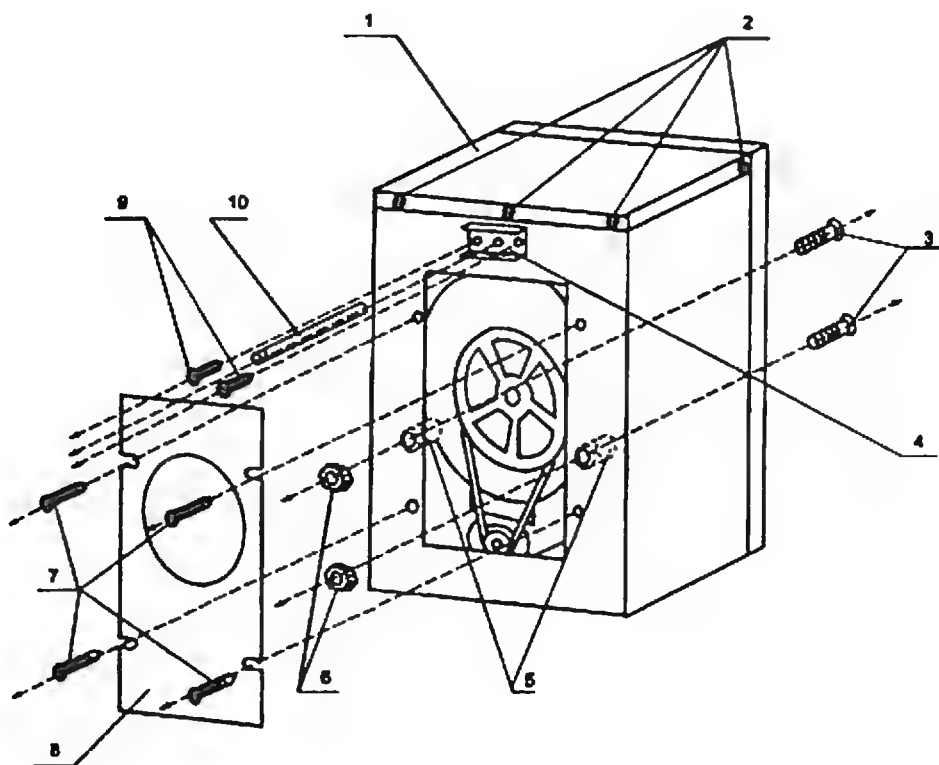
Демонтаж деталей, крепящих бак:
